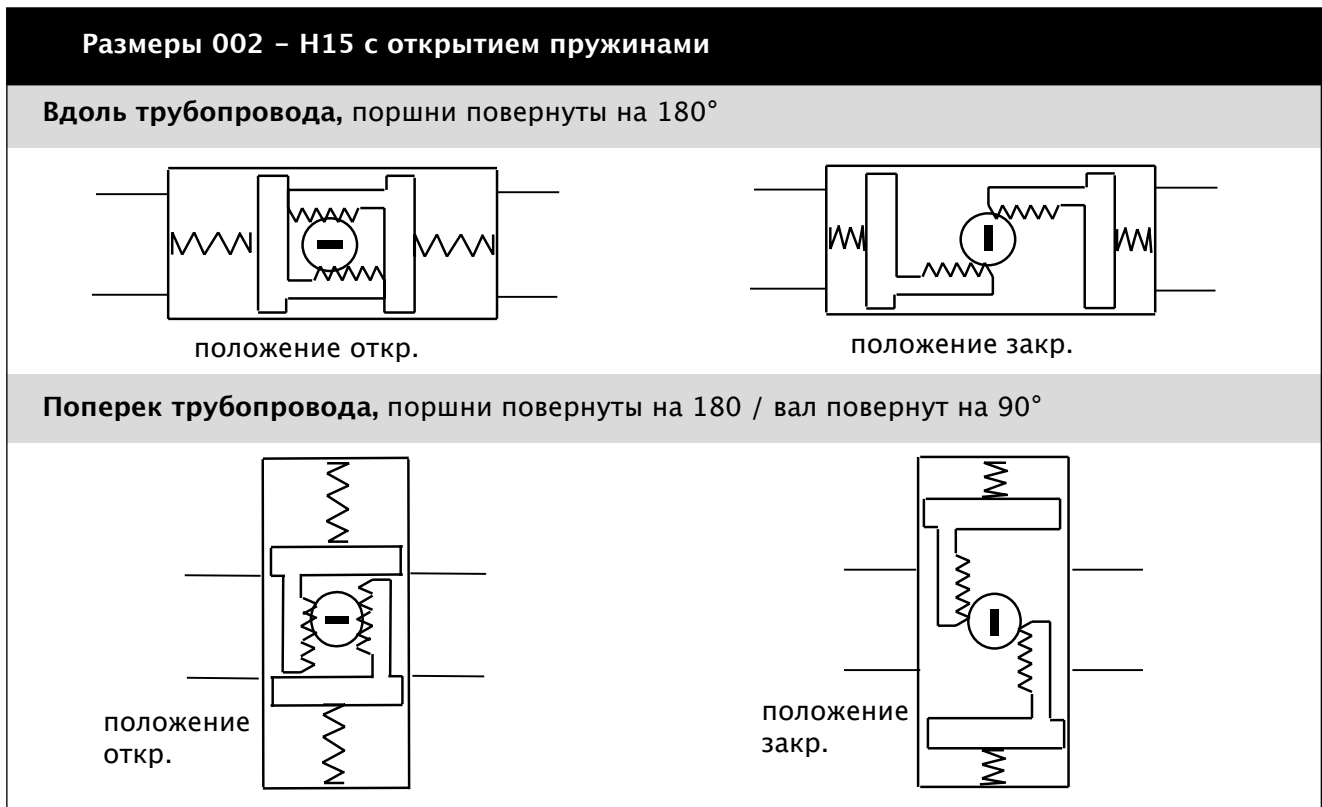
Схема привода с размыкающей пружиной (Размеры 002 до Н15)
